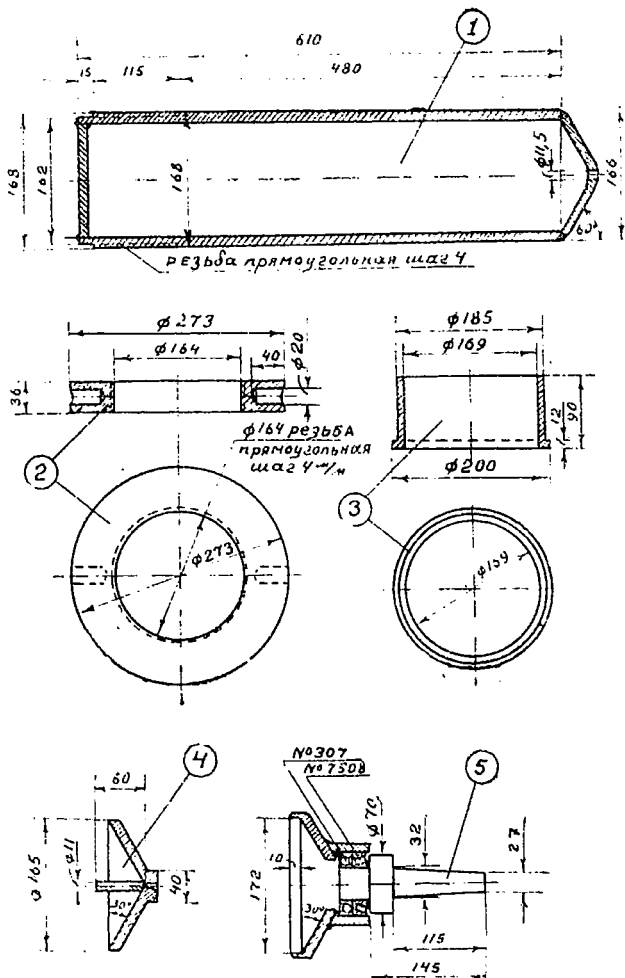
Приспособление для прокатки доильных ведер: 1 — оправка (шаблон); 2 — гайка; 3 — муфта; 4 — конусная оправка; 5 — внутренний центр.
